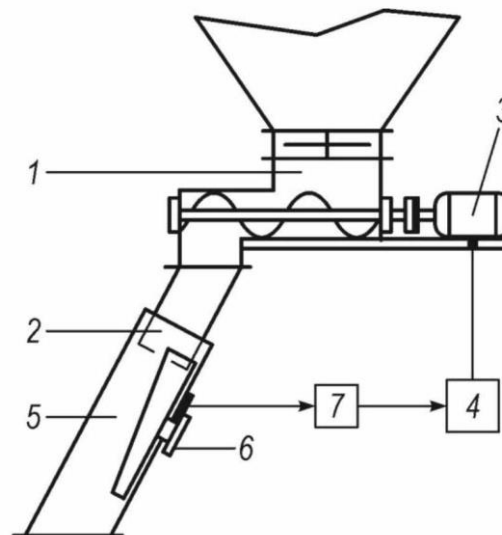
Принципова схема шнекового вагового дозатора
